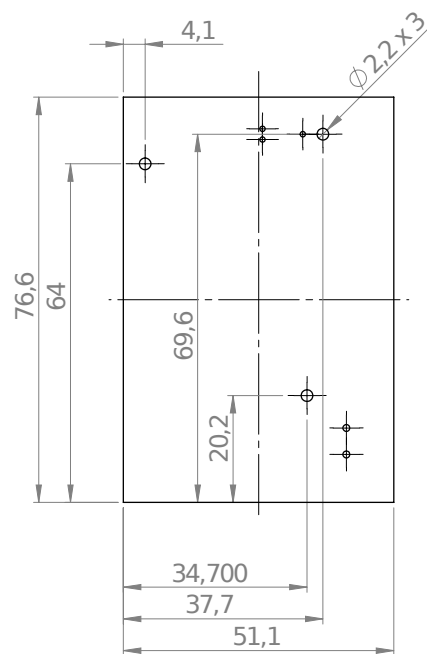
Außenabmessungen und Position der Bohrungen der Flugsteuerung
